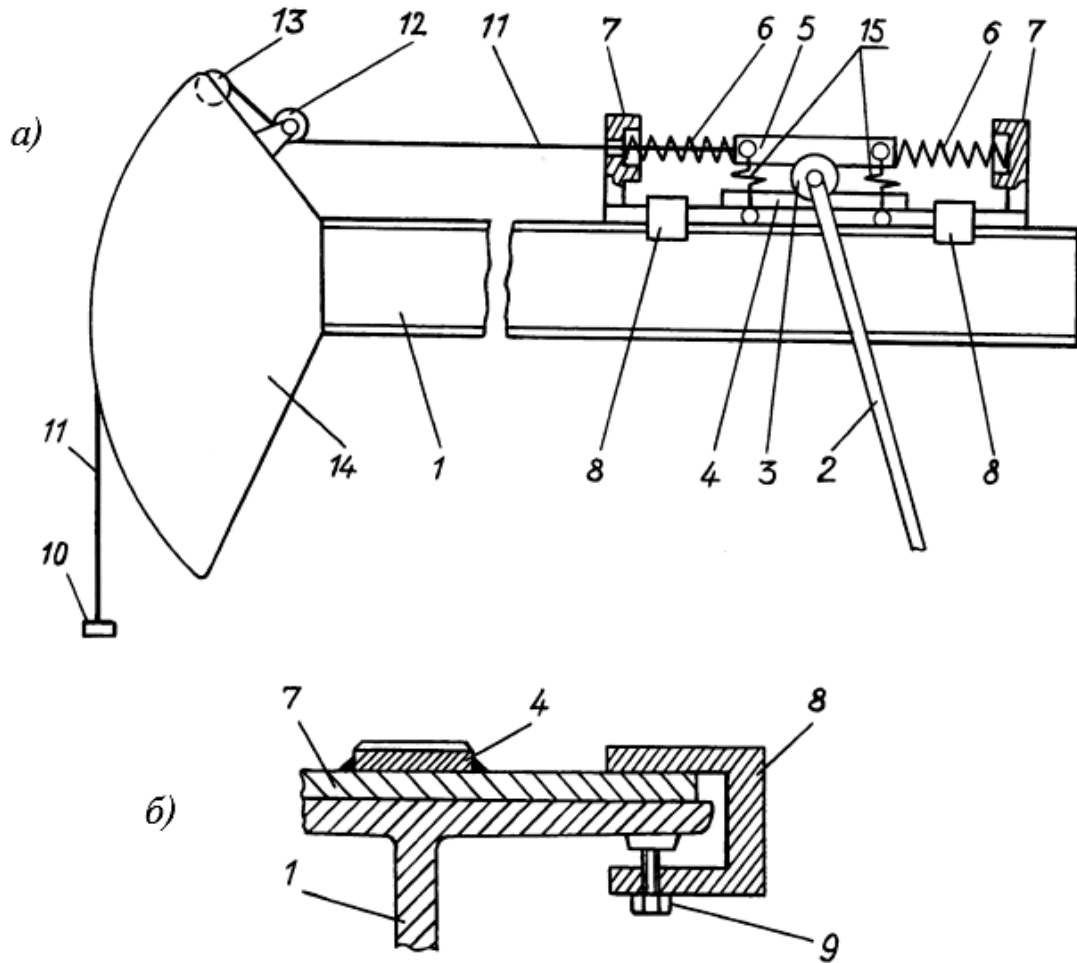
Схема конструкции балансира механизма станка-качалки с устройством для пружинного уравнивания:
